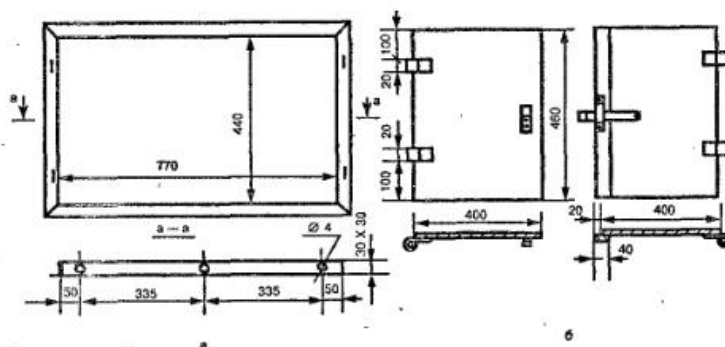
Дверца варочной камеры печи ИП-2. Размеры в мм
